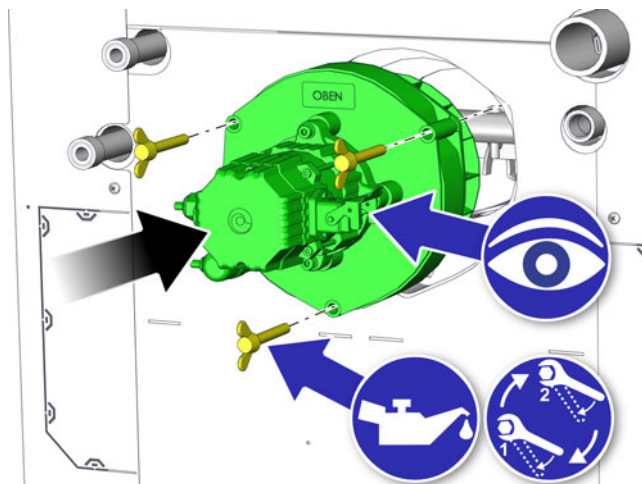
Nettoyage du rotor et remplacement du joint
